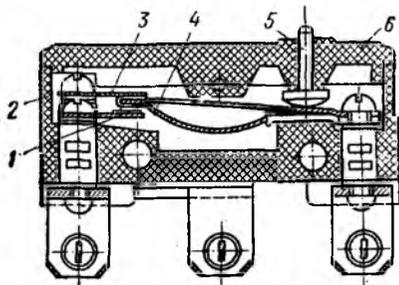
Микропереключатель МП-1: 1 и 3 — неподвижные контакты, 2 — корпус, 4 — подвижный контакт, 5 — шток, 6 — крышка
